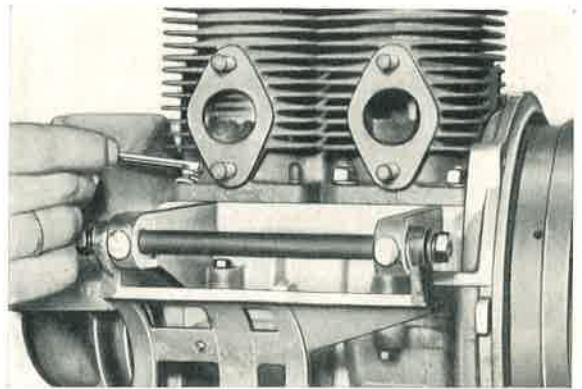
Die Zylinderfuß-Schrauben können nur mit einem Ringmutterschlüssel gelöst und angezogen werden.
